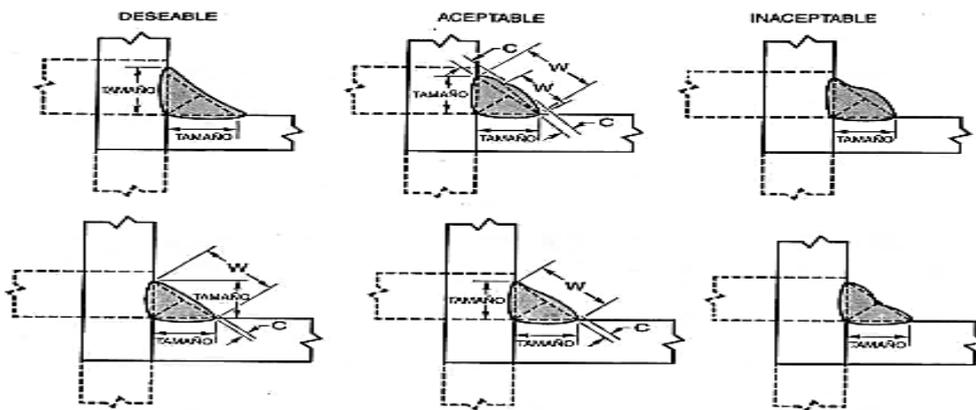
Perfiles de soldadura de canal juntas de esquina interior (ver tabla 4).
